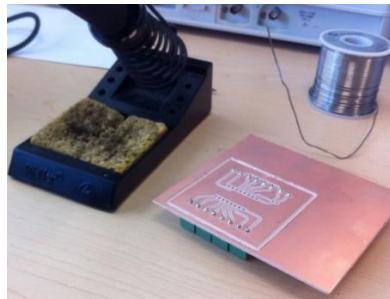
Soldado los componentes electrónicos de la PCB
